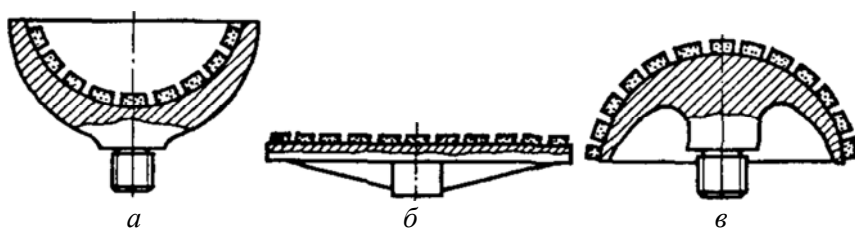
Алмазный инструмент в виде планшайбы (а), чашки (б) и гриба (в)
